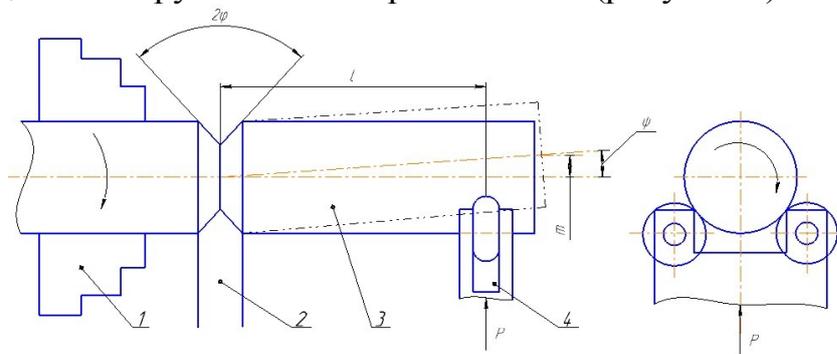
Схема разделения прутка на заготовки в токарном станке:
